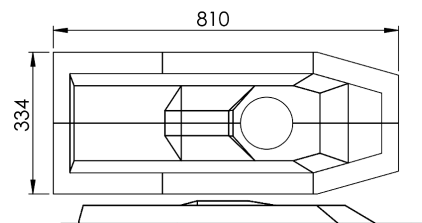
Ескізи креслення макету верхньої проекції корпусу БТР-80
